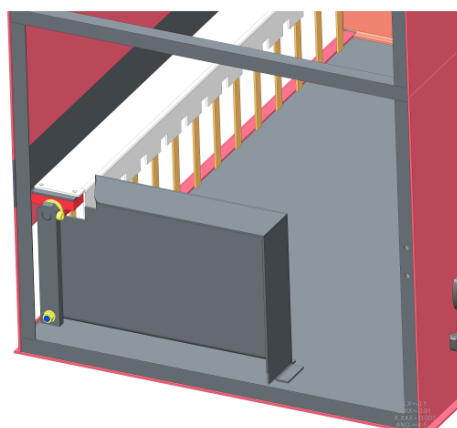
Rošt dna filtrační komory s usazenými pneumotory
